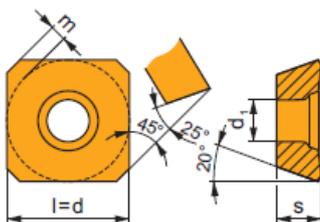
пластина для концевой фрезы ф. Pramet
